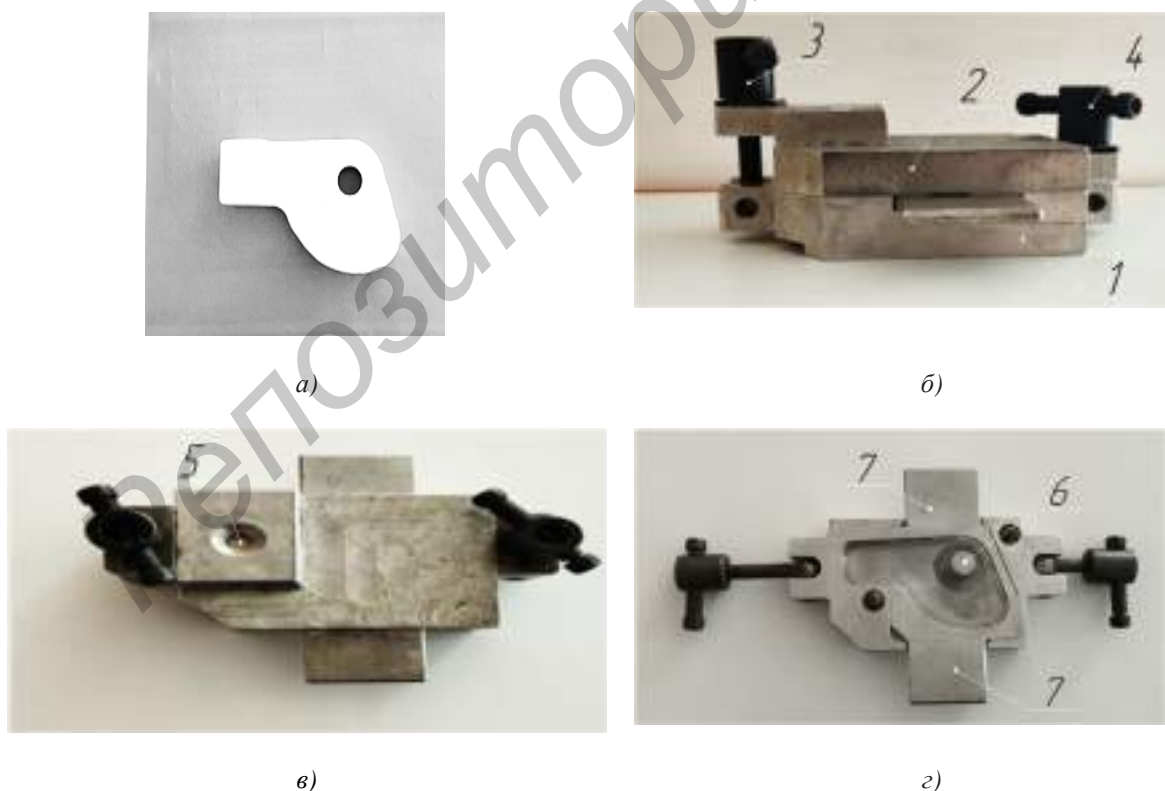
Конструкция приспособления для получения заготовки детали «кулачок»: а — деталь «кулачок»; б — главный вид приспособления; в — вид сверху; г — вид нижней матрицы
